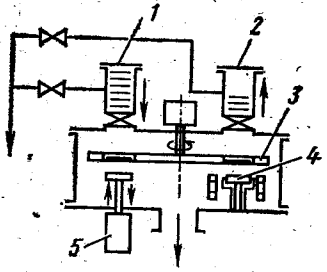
Установка полунепрерывного действия круговой компоновки с закрытой шлюзовой системой:
